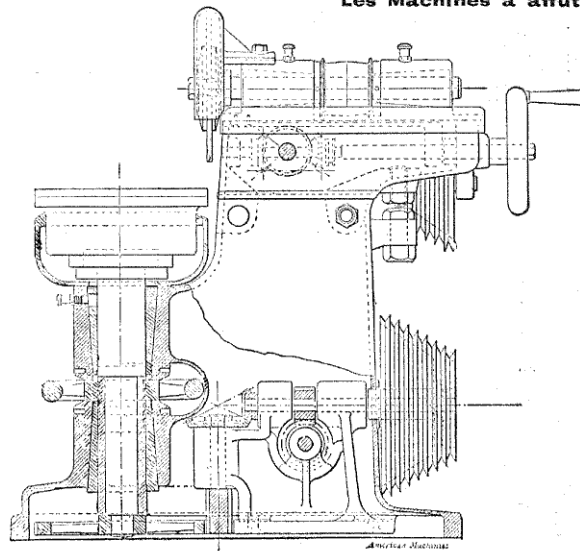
Élévation et section de la machine à rectifier circulaire Heald.
